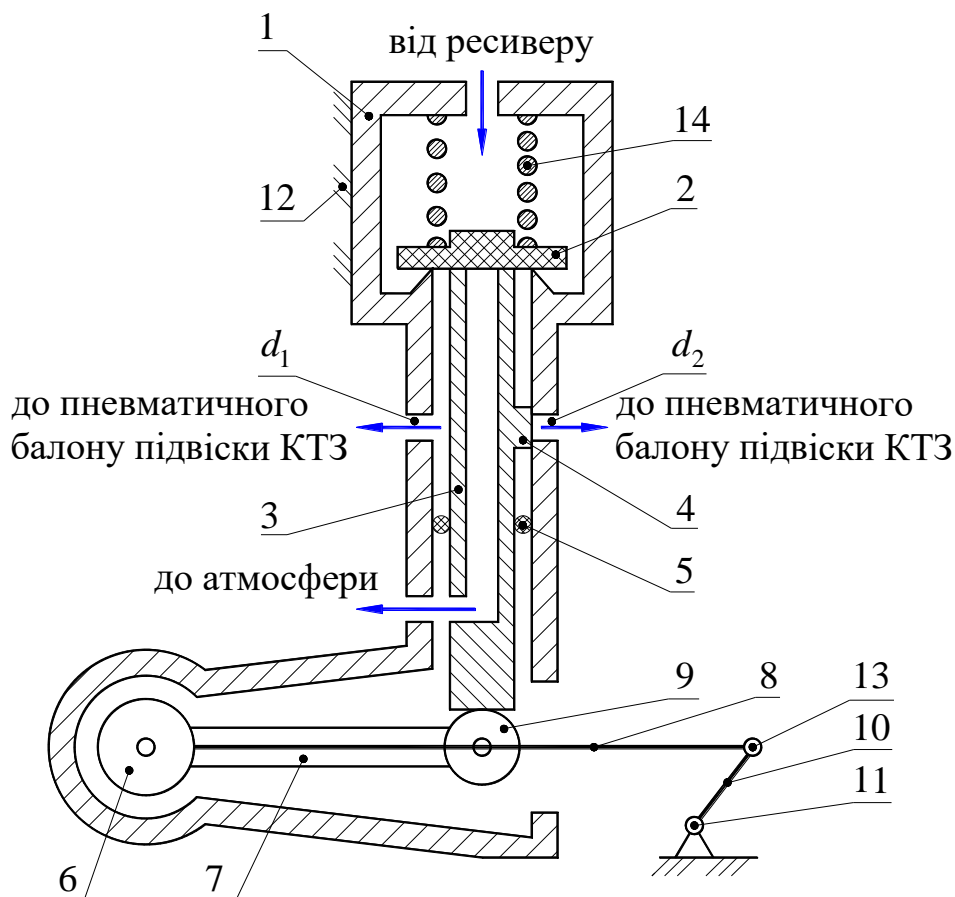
Принципова схема двоступеневого регулятора рівня підлоги пневмопідвіски автомобіля: 1 - корпус; 2 - двохсідельний клапан; 3 - плунжер; 4 - поясок другого ступеня РРП; 5 - ущільнення плунжера в корпусі; 6 - поворотна вісь важелів; 7 - важіль штовхача плунжера; 8 - привідний важіль; 9 - сферична опора-штовхач плунжера; 10 - тяга; 11 - шарнірне кріплення тяги до мосту автомобіля; 12 - кріплення корпусу до кузова автомобіля; 13 - шарнірне з'єднання приводного важеля 8 та тяги 10; 14 - пружина двохсідельного клапану
